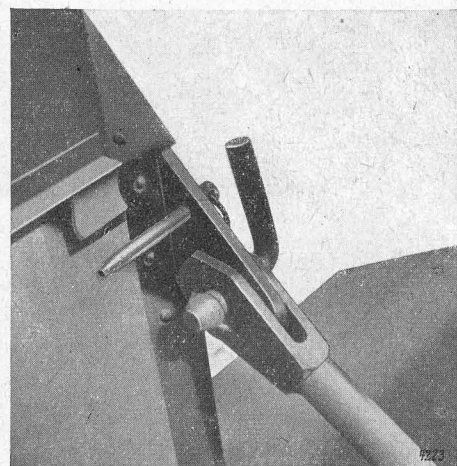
Befestigung der Zugstange am Bedienungshaus.
